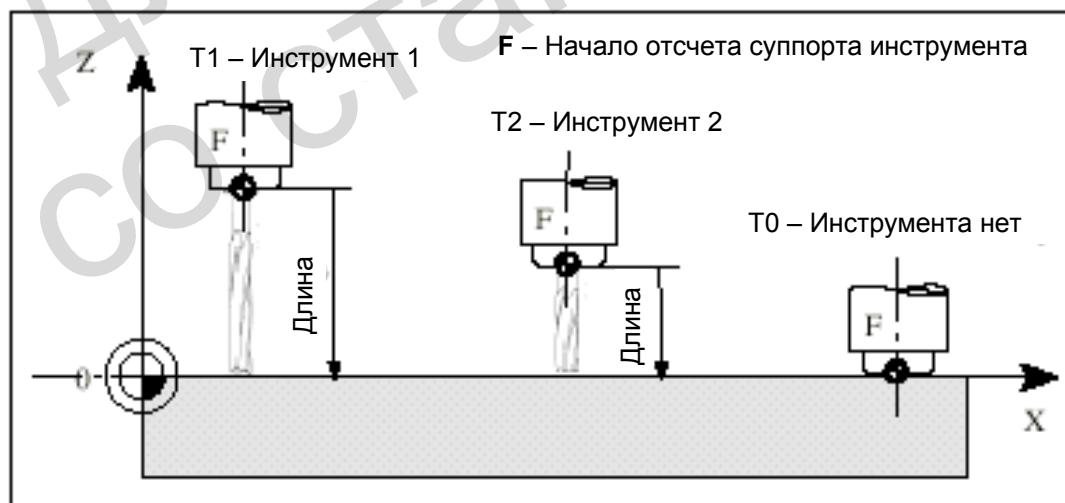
Движение к позиции детали Z0 – различная коррекция длины
